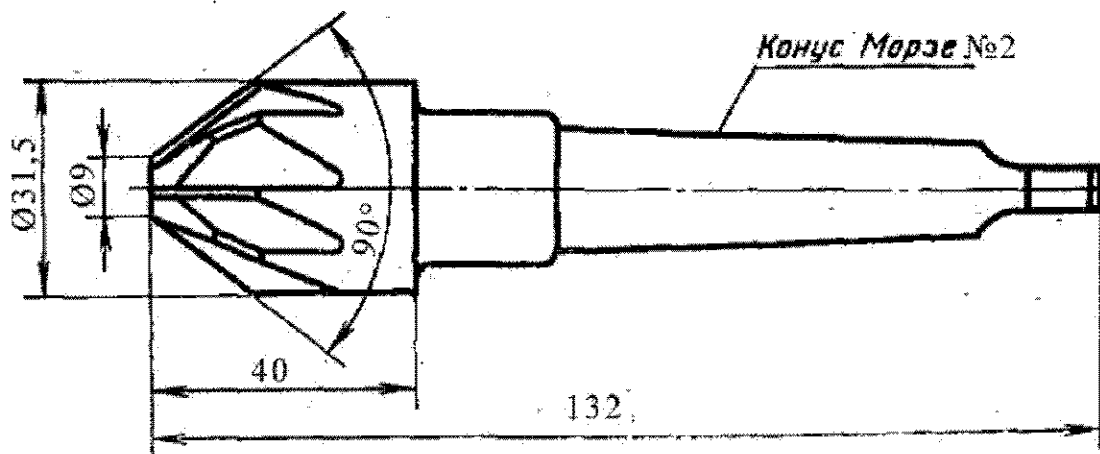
Зенковка 2353-0124 ГОСТ 14953-80
